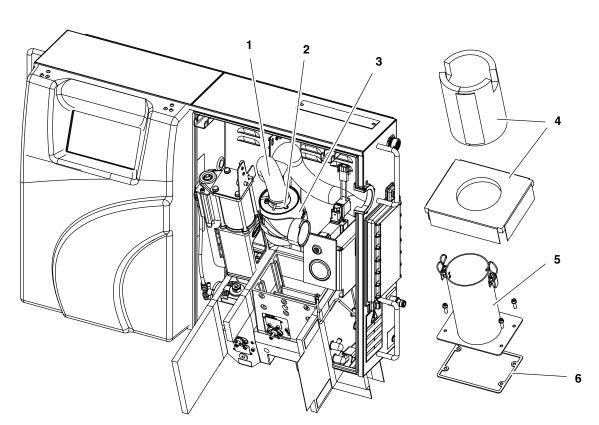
Komponenten der Zyklonbaugruppe austauschen
